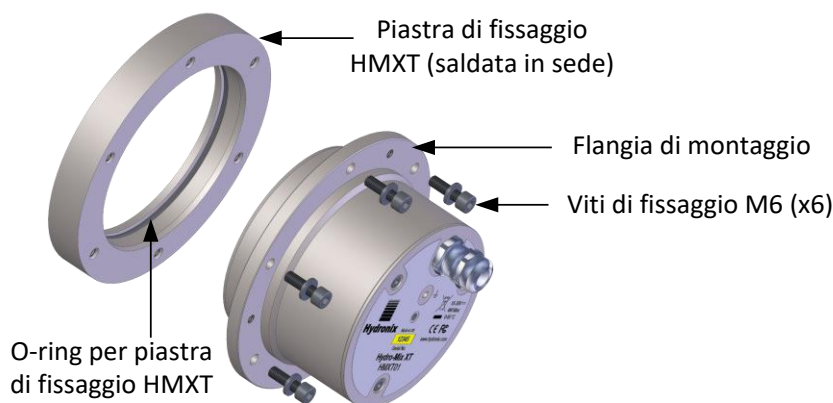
Hydro-Mix XT collegato alla piastra di fissaggio HMXT
